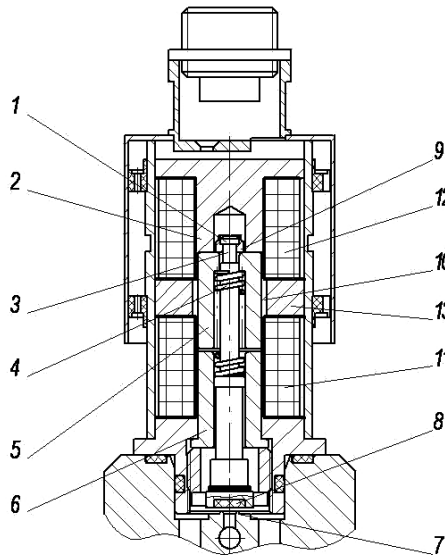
Конструктивна схема клапана з двопозиційним електромагнітним приводом: 1 – головка штока; 2 – корпус електромагніта (верхній стоп); 3 – шийка штока; 4 – буферна пружина; 5 – повзун (якір); 6 – нижній стоп; 7 – сідло; 8 – золотник; 9 – стопорна шайба; 10 – розподільна трубка; 11 – обмотка закриття клапана; 12 – обмотка відкриття клапана; 13 – постійний магніт.
